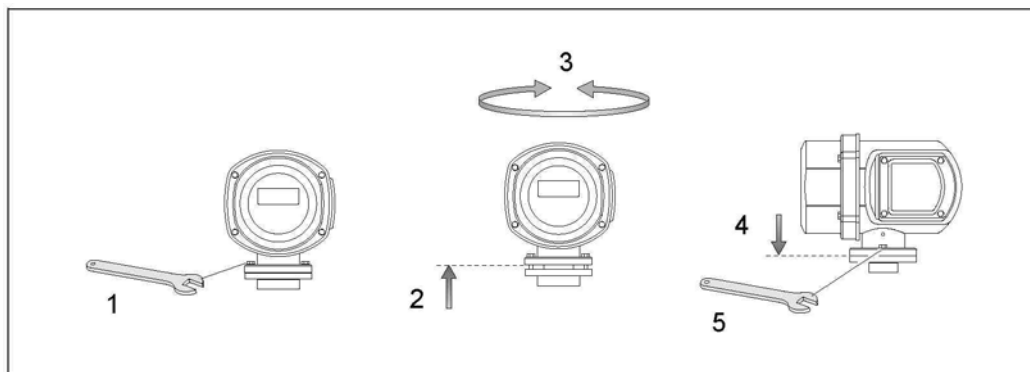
Вращение корпуса преобразователя (полевой корпус из нержавеющей стали)
